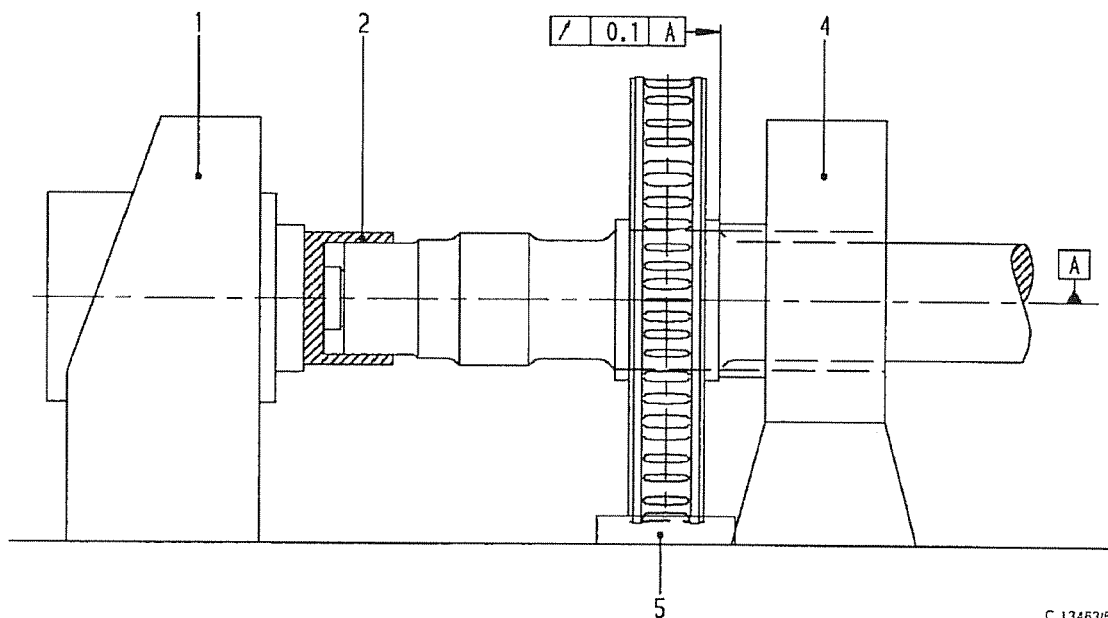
Резьбовое соединение для метода отпрессовки SKF
